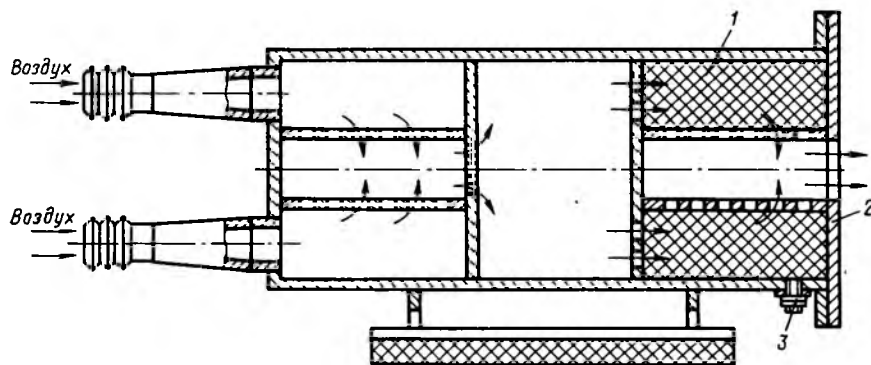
Глушитель выхлопа пневмопривода перемещения каретки многоэлектродной сварочной машины АТМС — 14×75
